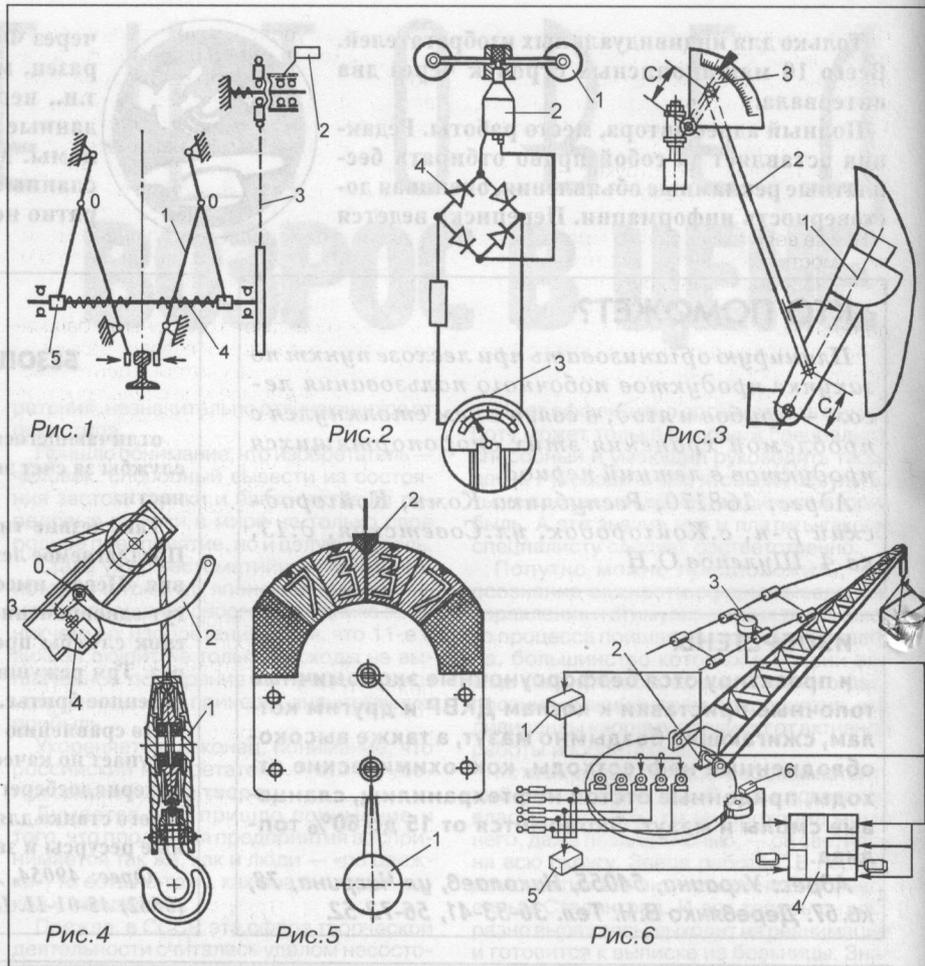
Противоугонное устройство. 1 — рычаги, усиливающие давление тормозных башмаков на головку рельса; 2 — привод устройства; 3 — цепная передача с ведущей звездочкой; 4 — ходовой винт с правой и левой резьбой; 5 — ходовые колодки.
